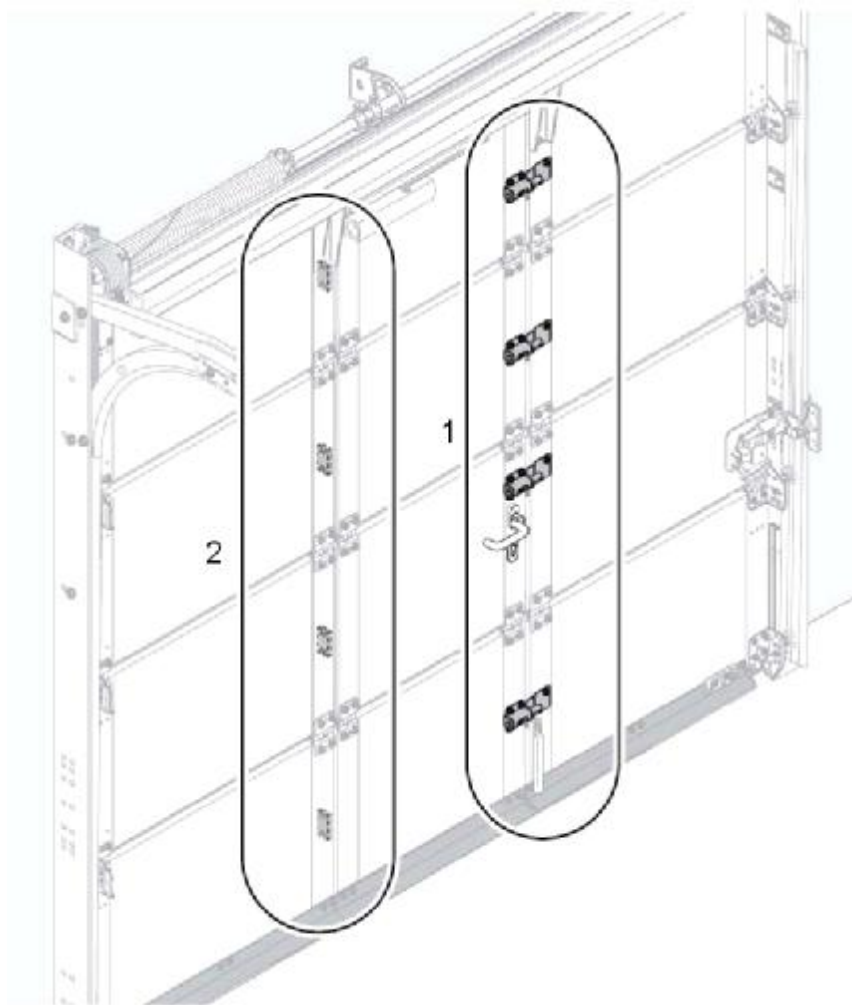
Widok bramy segmentowej garażowej podnoszonej bez napędu mechanicznego
